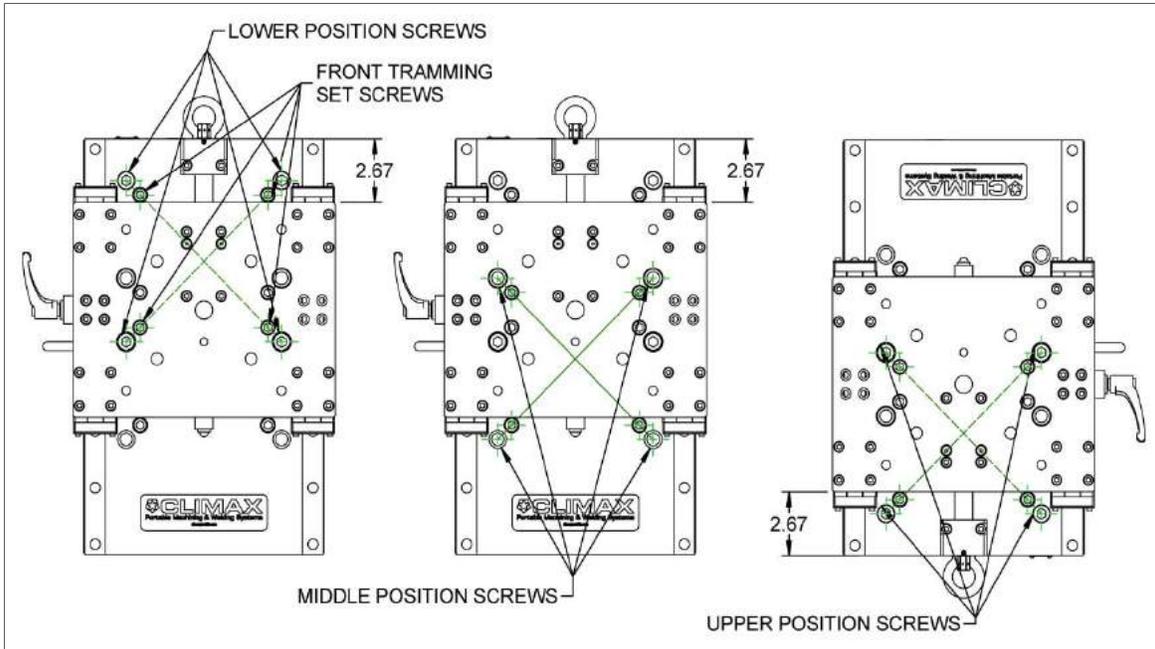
Orificios para tornillos de montaje deslizante en el eje Z
